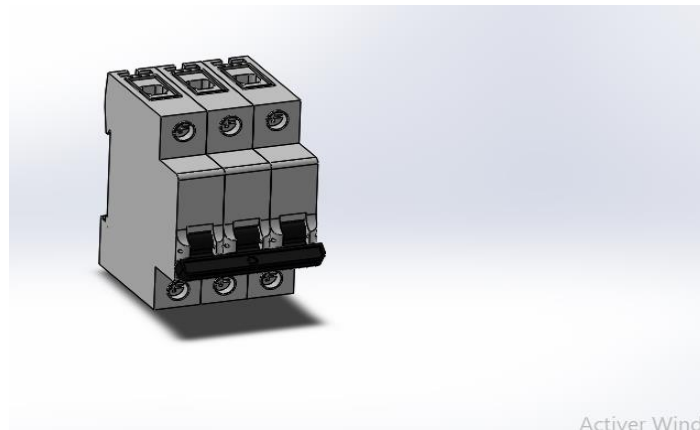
Dessin de disjoncteur en 3D par SOLIDWORKS
